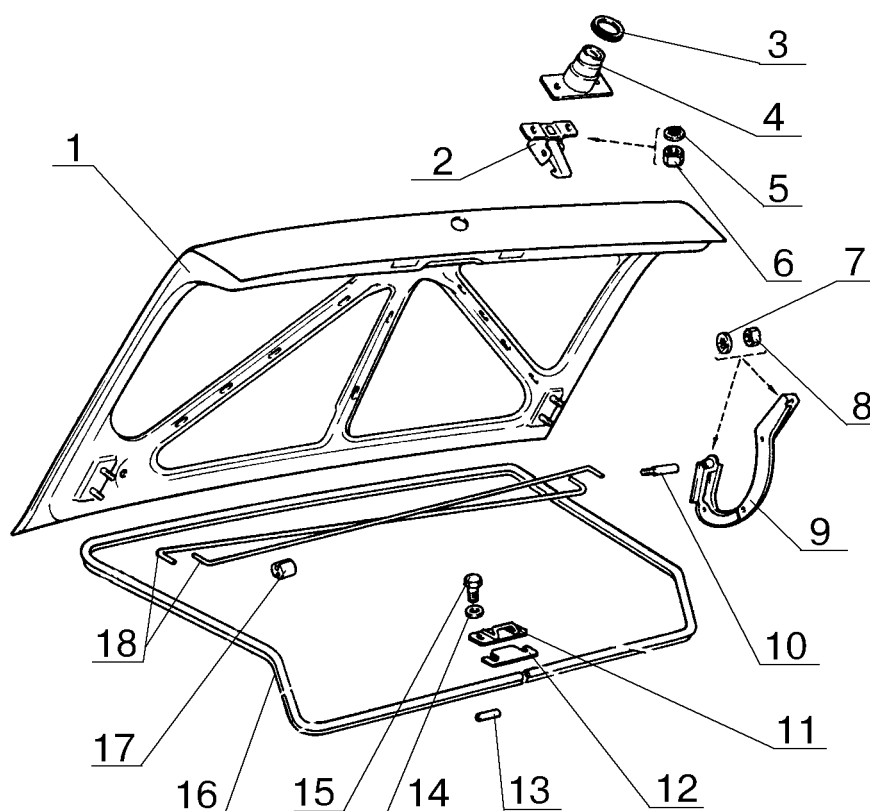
Крышка багажника автомобиля ВАЗ-21099 и ее механизмы:
